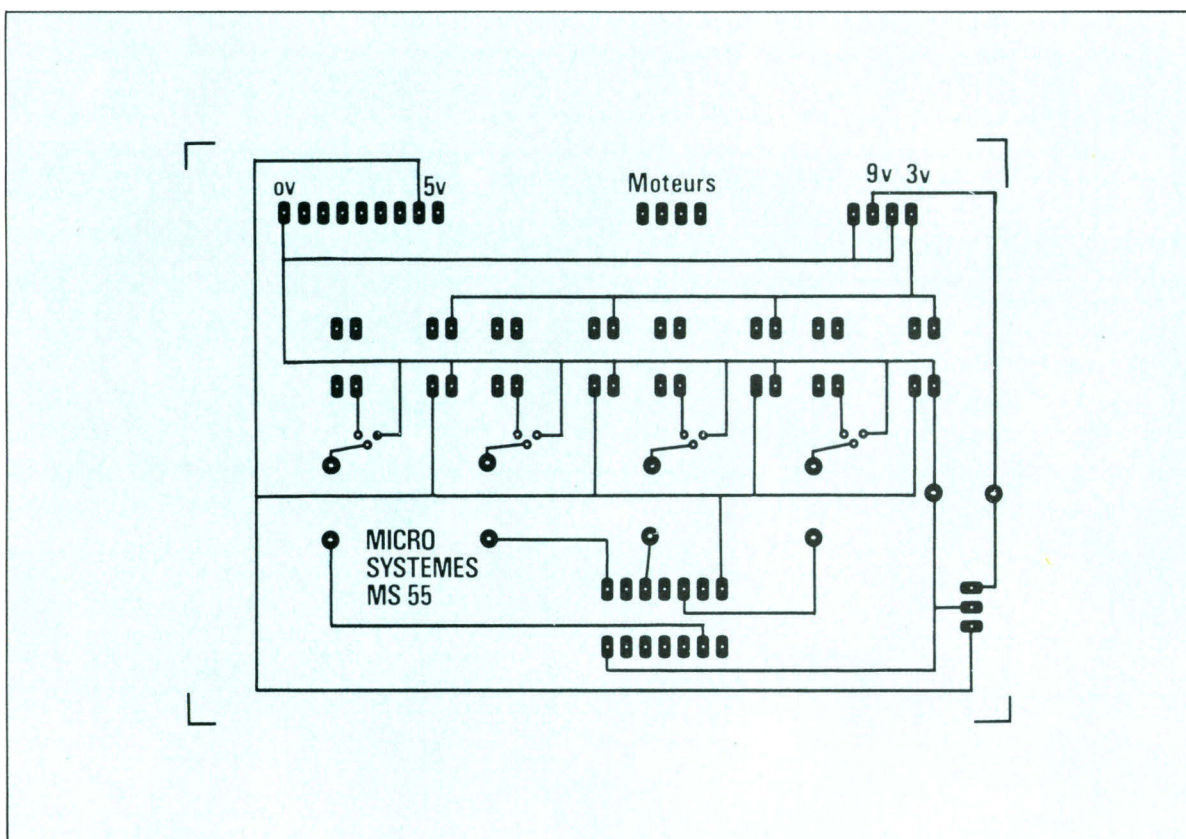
Circuit imprimé côté soudures.
